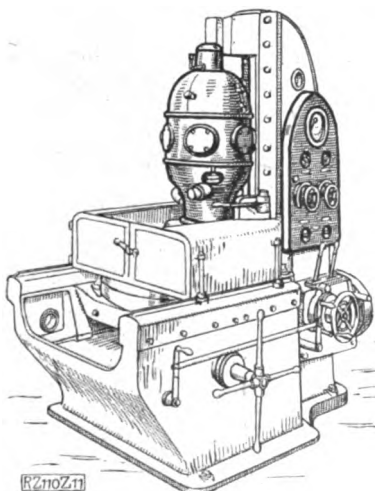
Flächenschleifmaschine; Motor auf der Spindel, besondere Motoren für Vorschub und Pumpe.
